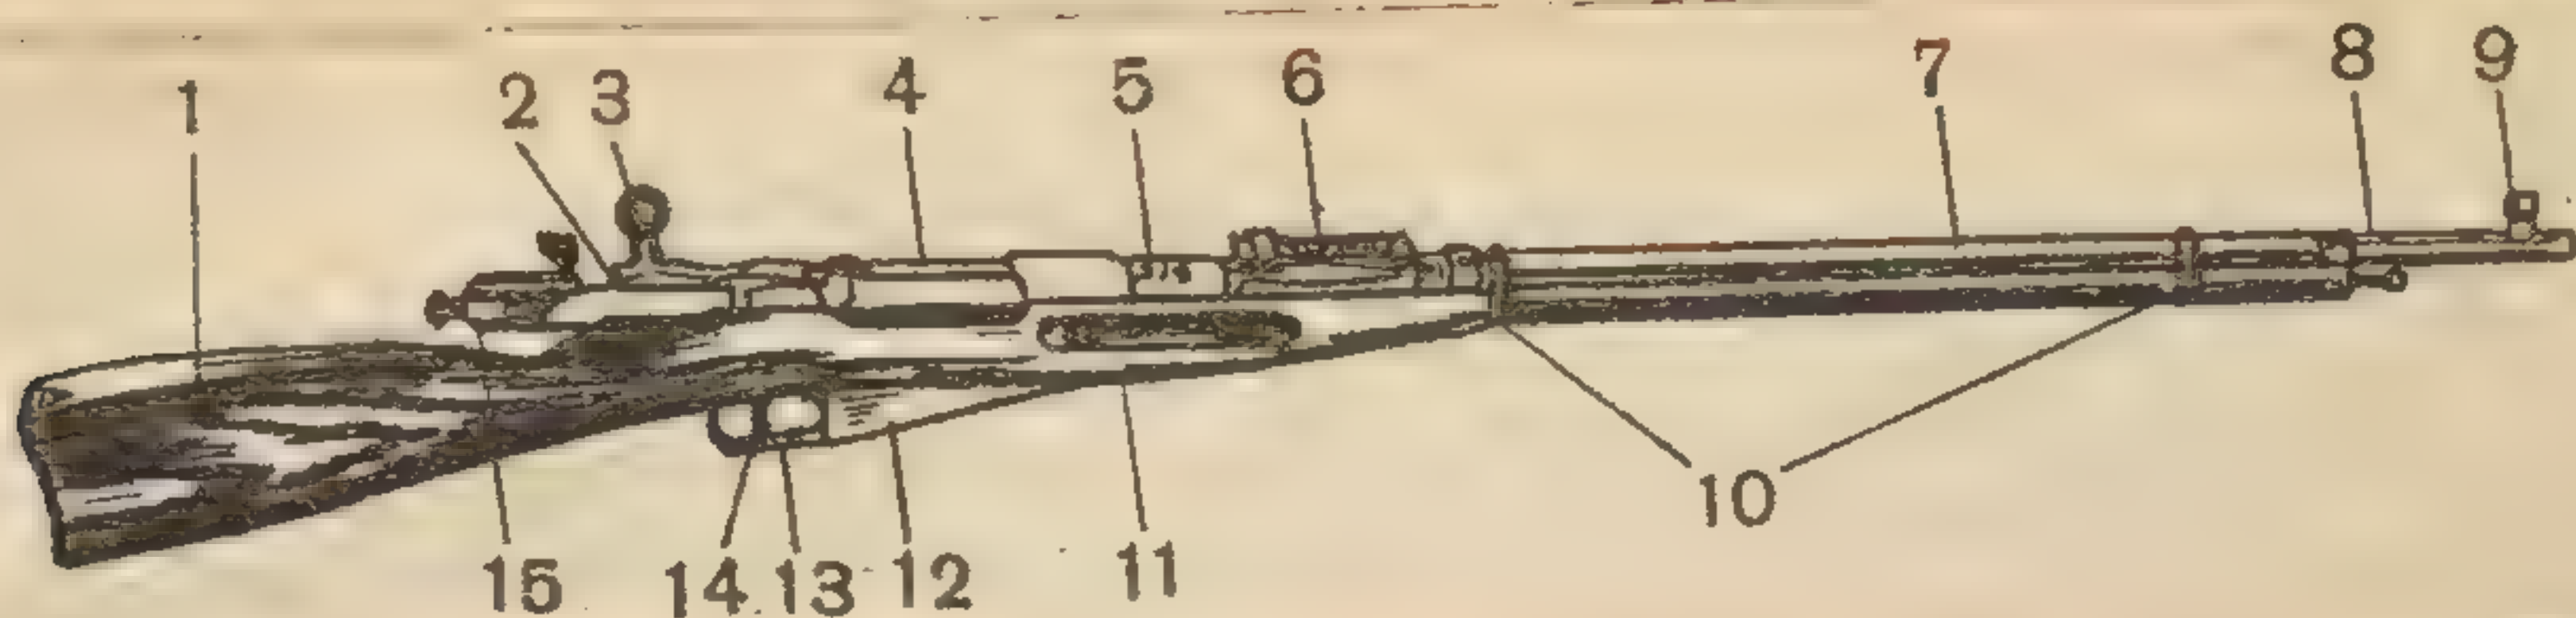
Винтовка образца 1891—1930 года (калибр 7,62 мм)
